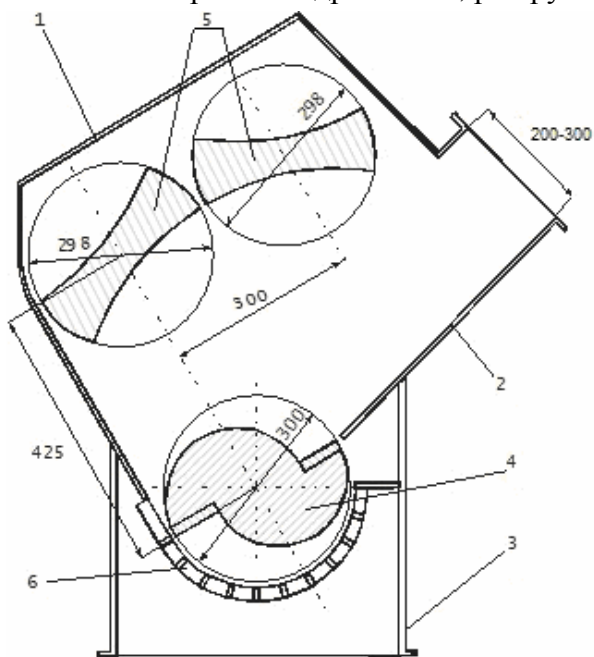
Схематическая конструкция дробилки ДАУ-250: 1 – корпус дробилки; 2 – загрузочный патрубок; 3 – разгрузочный отсек; 4 – первичный ротор; 5 – вторичные ротора; 6 – разгрузочное решето
